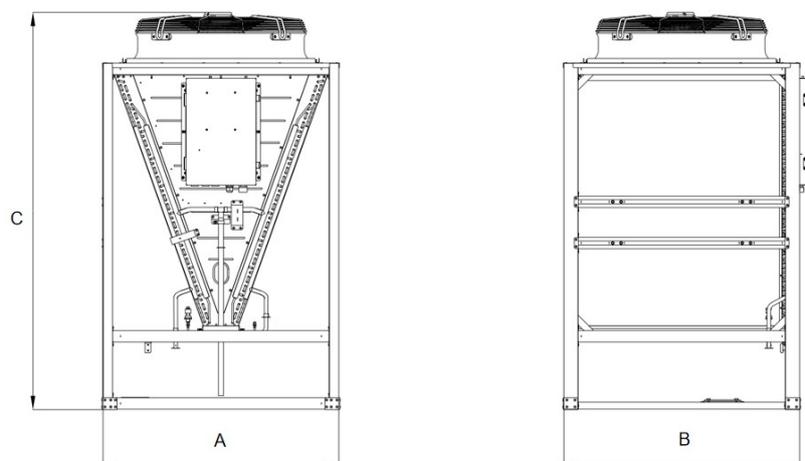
Габаритные размеры централизованного конденсатора серии CS – обычный вентилятор
